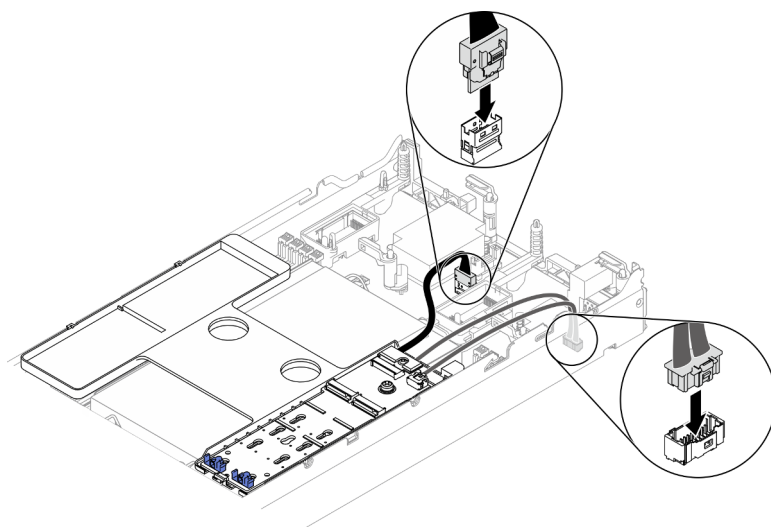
Connexion des câbles du fond de panier M.2 à la carte mère
